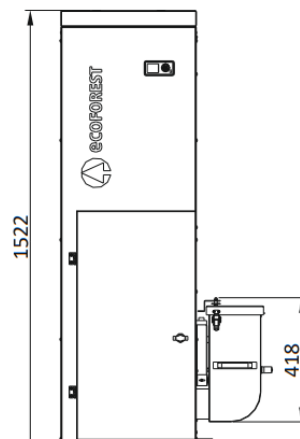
Alzado acotado da caldeira VAP 5-20. Fonte: Ecoforest.
